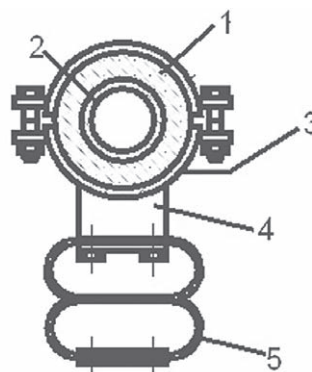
Виброизолирующая подвеска судовых трубопроводов ПТАП:
